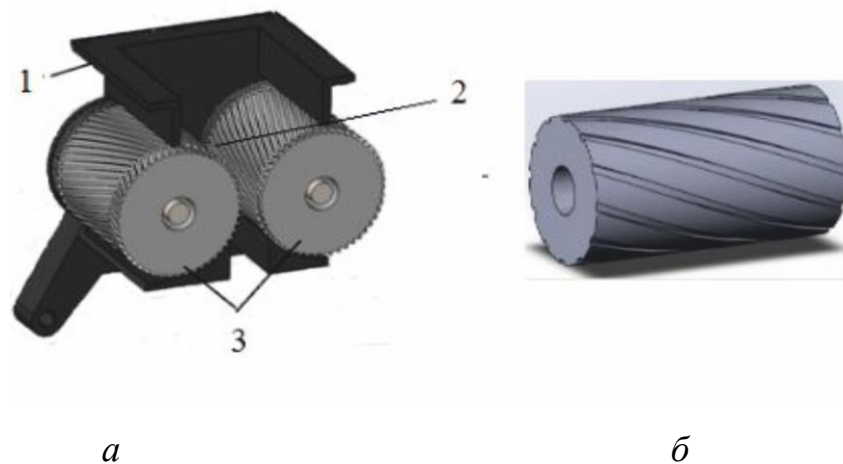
Вузол нагнітання: 1-місткість для тіста; 2- міжвалковий зазор; 3- валки (а); загальний вигляд нового валка (б)
